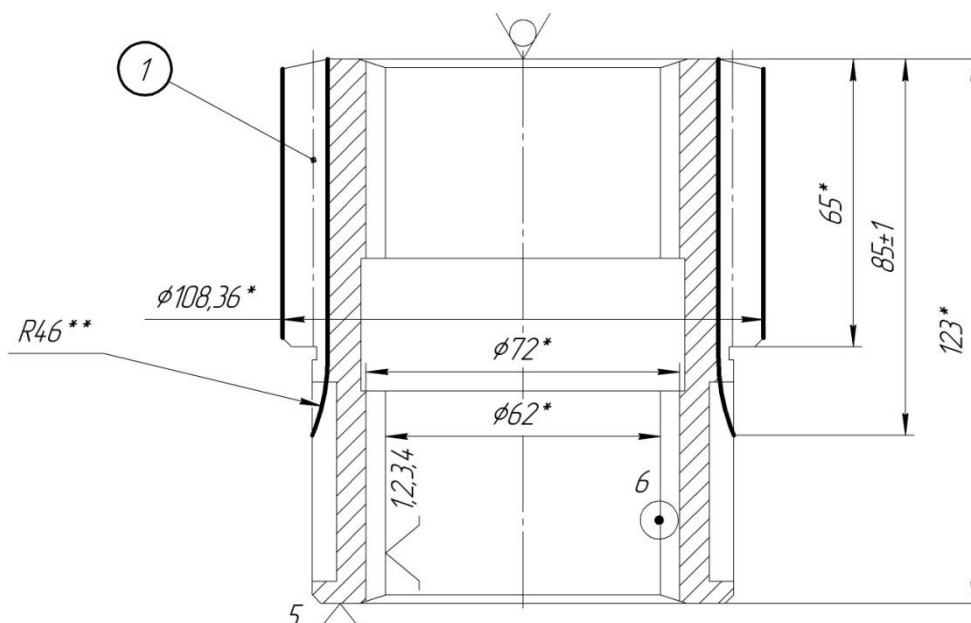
Ескіз зубофрезерної операції 045
